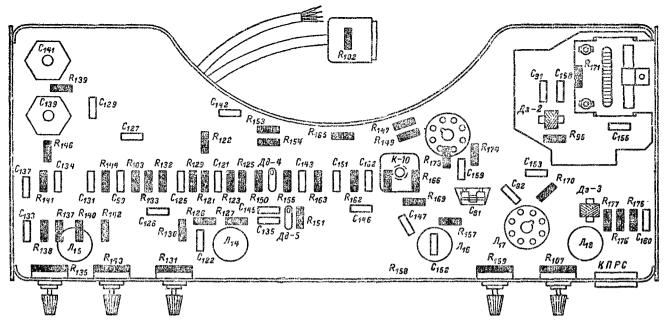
Расположение деталей на шасси блока развертки телевизора «Радий-Б» (вид со стороны монтажа).
